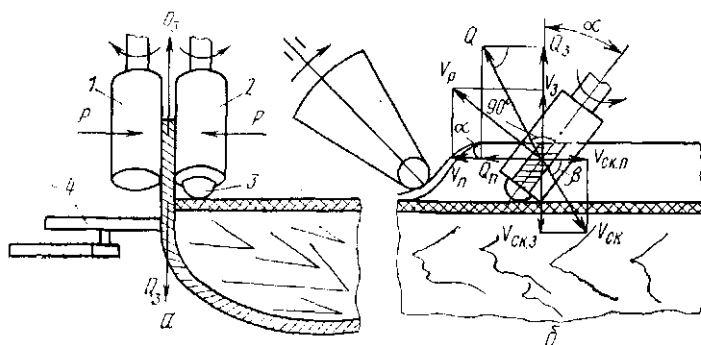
Схема исполнительных органов машины для затяжки заготовки верха обуви роликами
